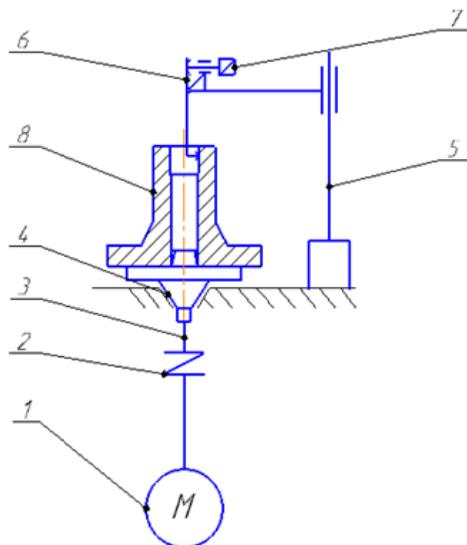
Схема контрольного приспособления для проверки радиального биения выточки диска
